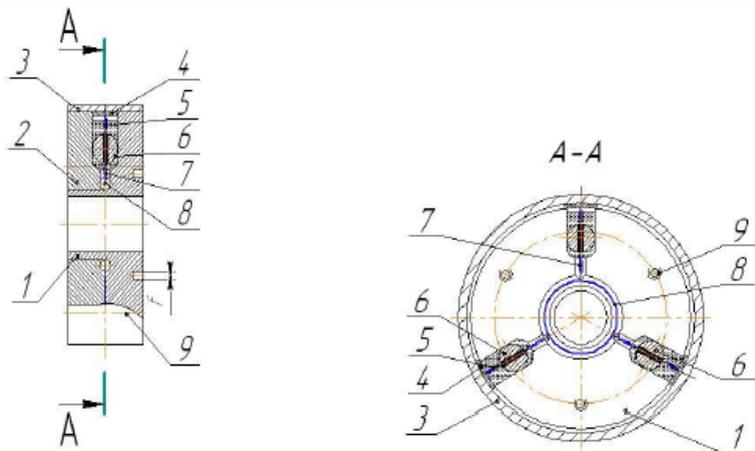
Общий вид устройства для автобалансировки заготовок
